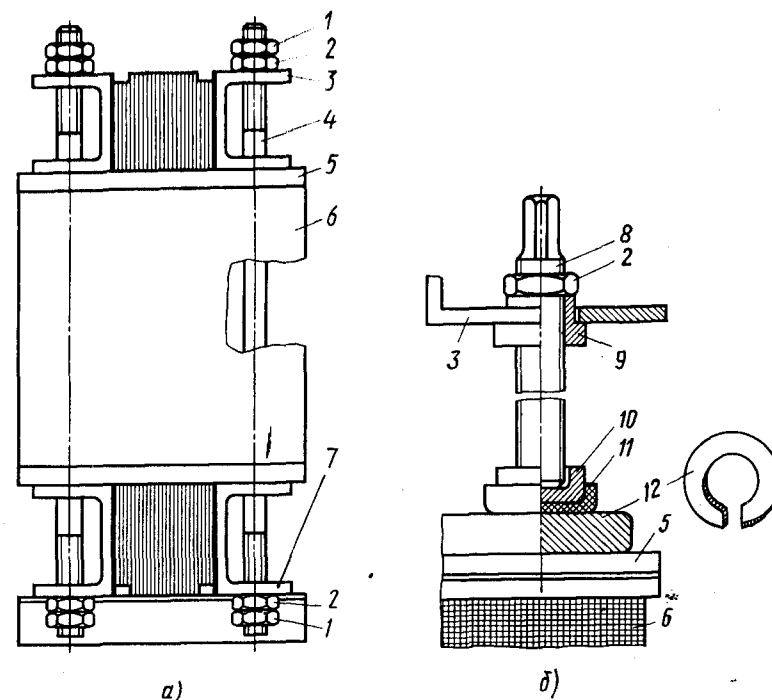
Прессовка обмоток вертикальными шпильками и ярмовыми балками (а) и прессующими кольцами (б):
